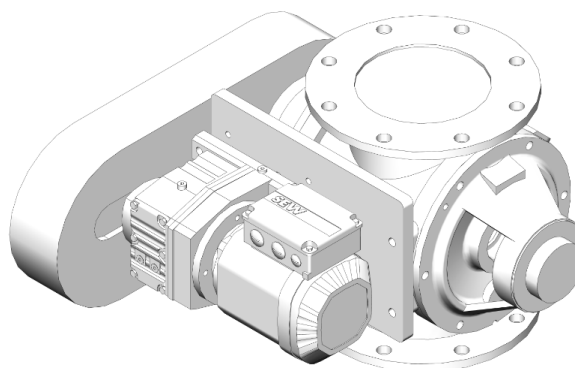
Kjodemotor (sy R-motorer med kjetting)
